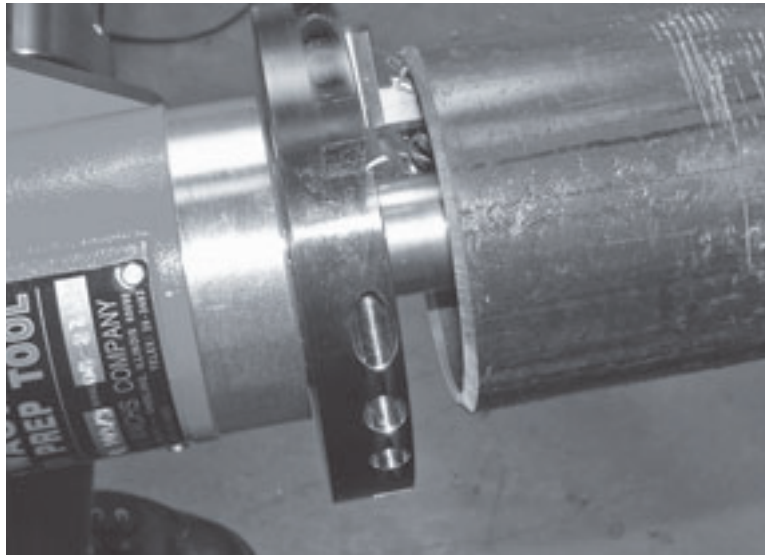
Lassen Sie die Maschine laufen, bis die gewünschte Innenbearbeitung erreicht ist.
